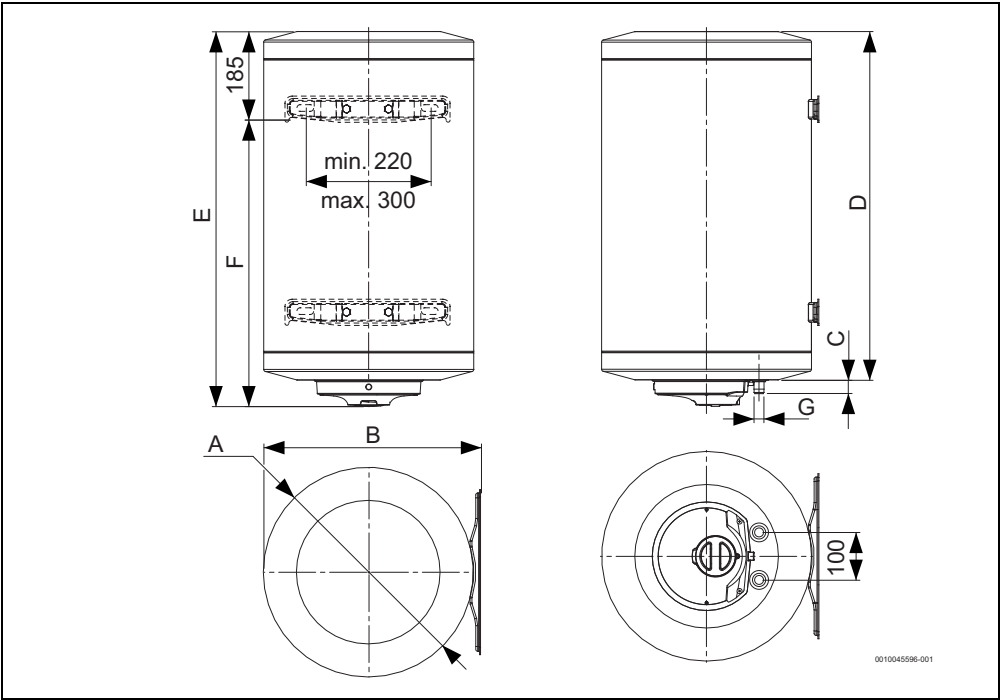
Dimensions en mm (montage mural, installation verticale)
